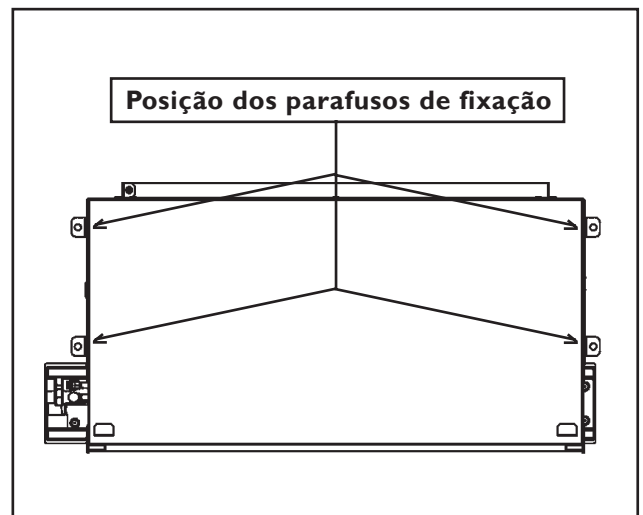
MONTAGEM DO SUPORTE DE FIXAÇÃO
